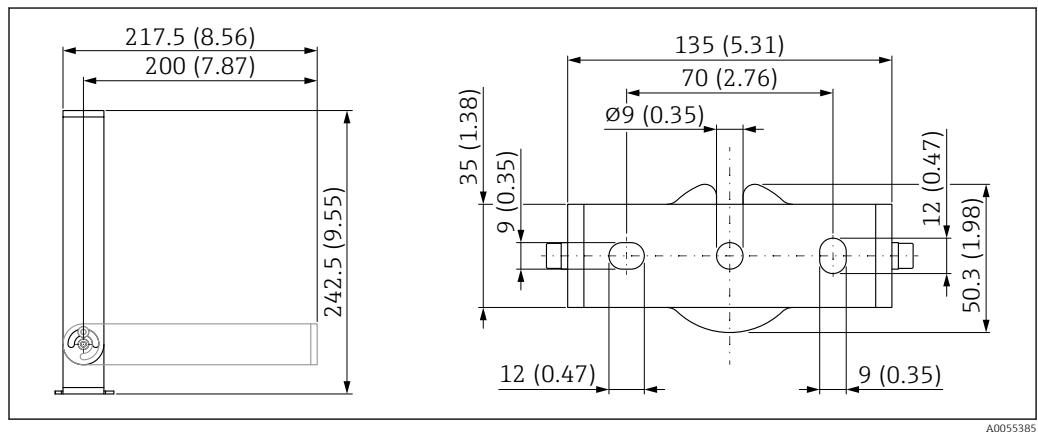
Dimensioni della staffa di montaggio. Unità di misura mm (in)
